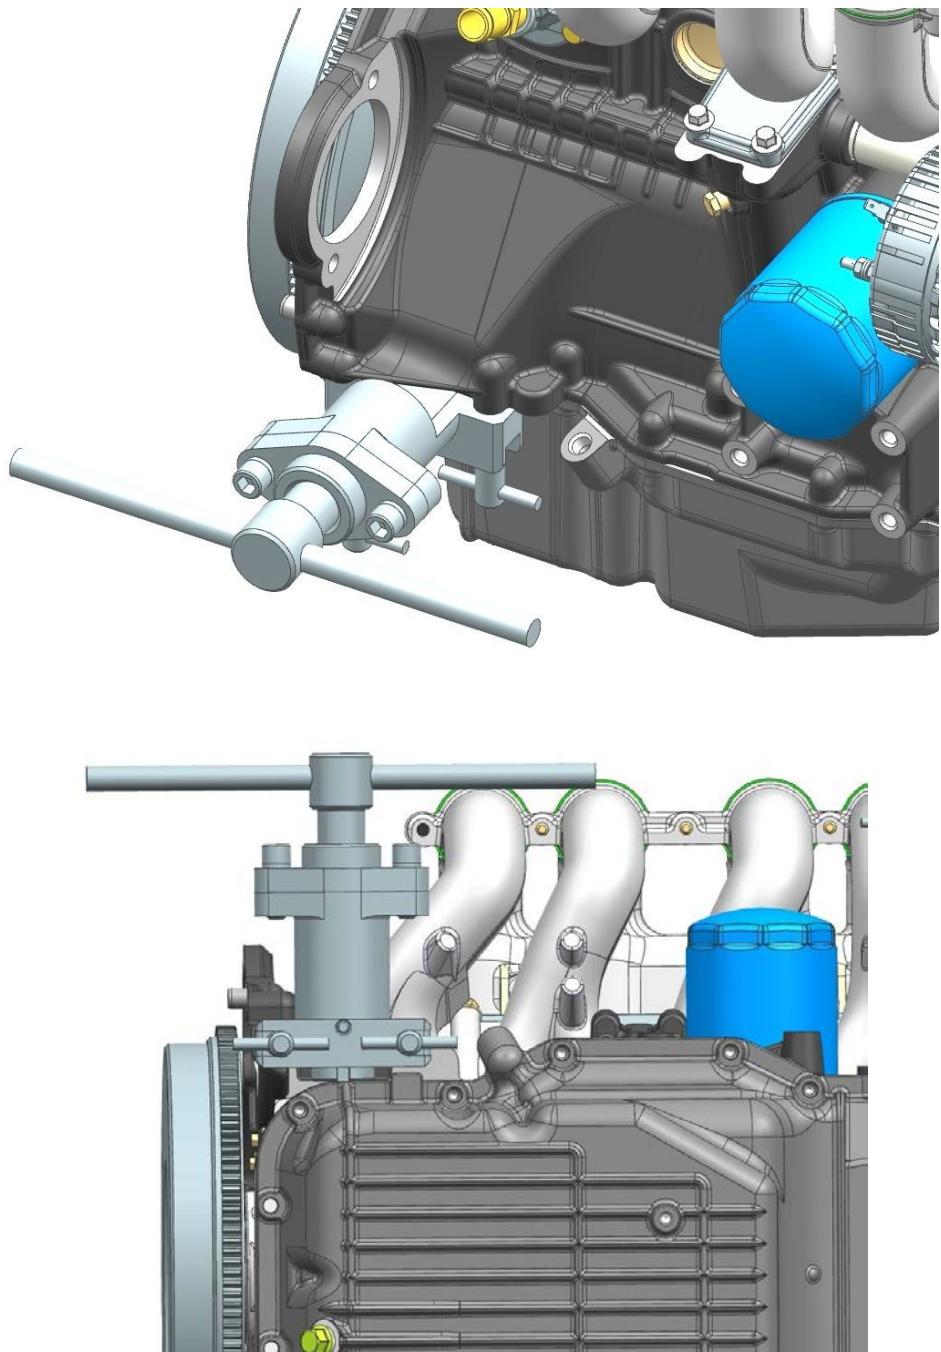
Установка приспособления ЗМ 7823-4815 на двигатель
